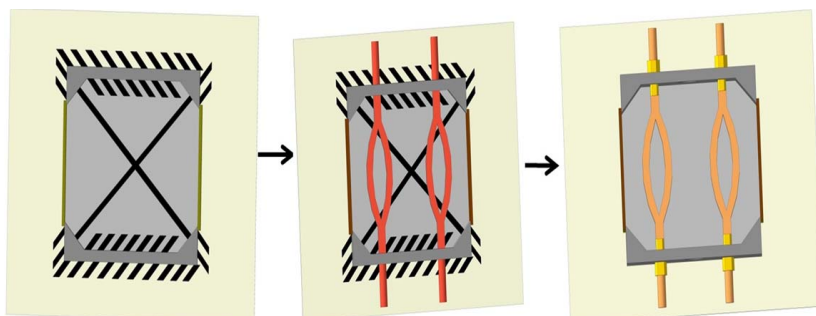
Схематичное изображение основных технологических этапов изготовления станины (вид сверху)
